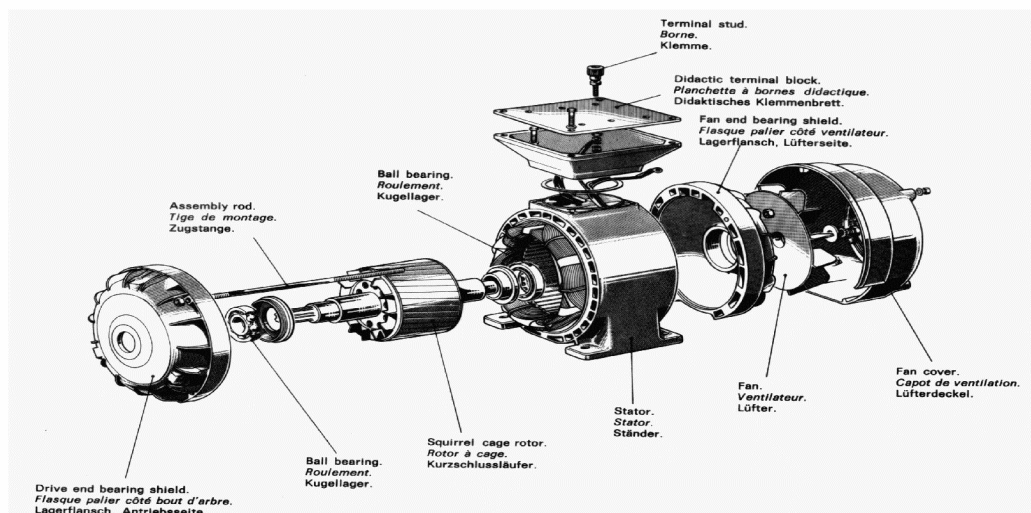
Éléments constituant une machine asynchrone à cage d'écureuil [3].
